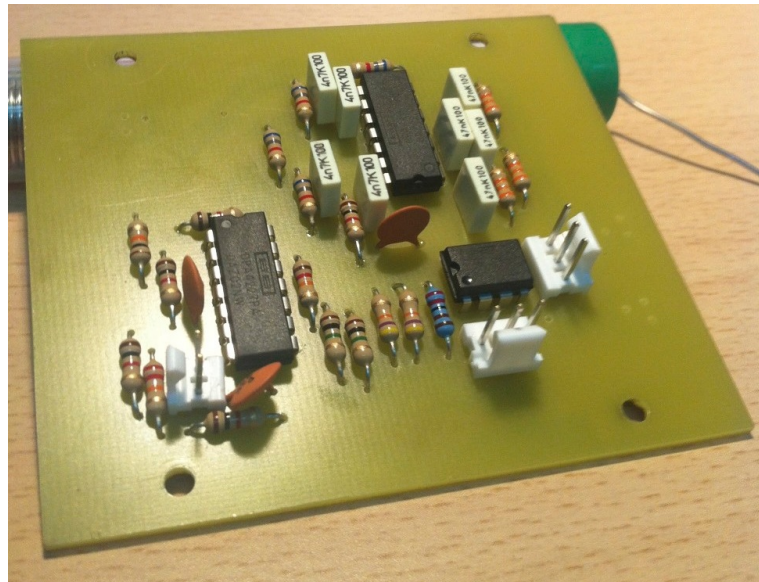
Fotografía del circuito con los componentes electrónicos soldados.
